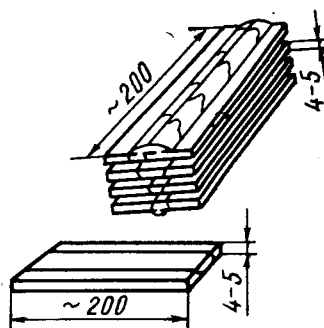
Схема разрезки заготовки на послойные макрошлифы
